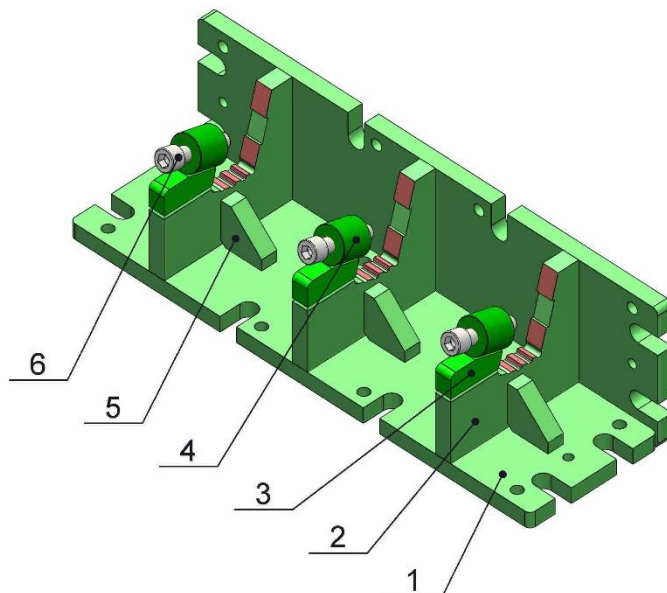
Общ вид на приспособлението за механично обработване на първа установка.
